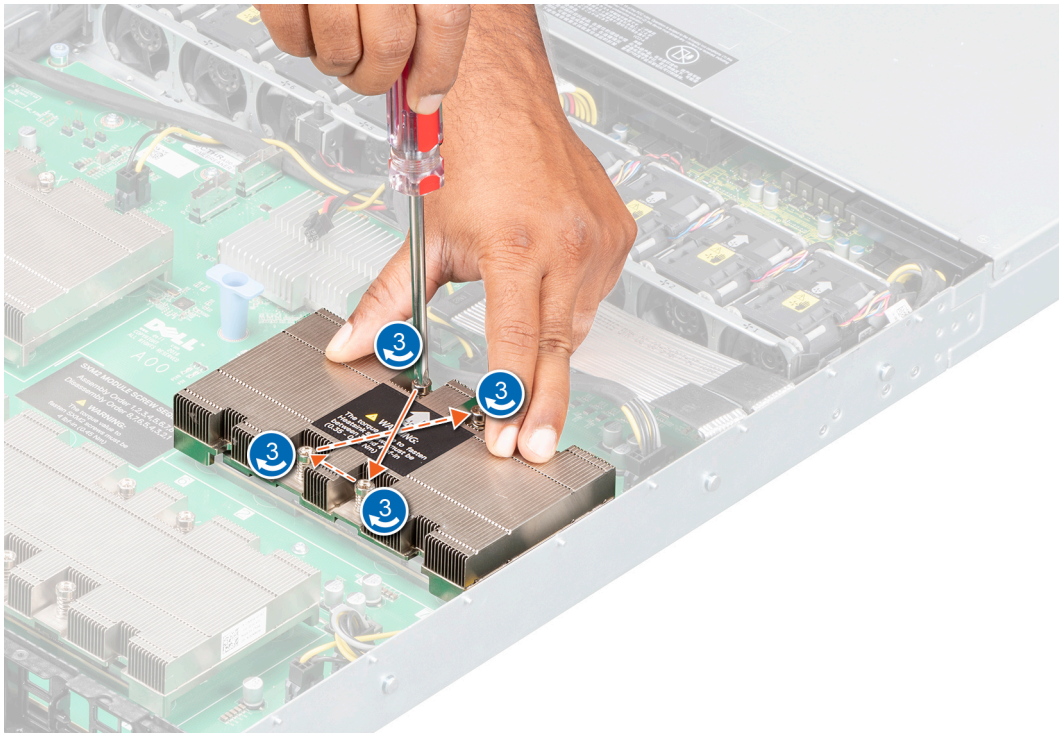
Installieren der SXM2-GPU-Kühlkörperschrauben
